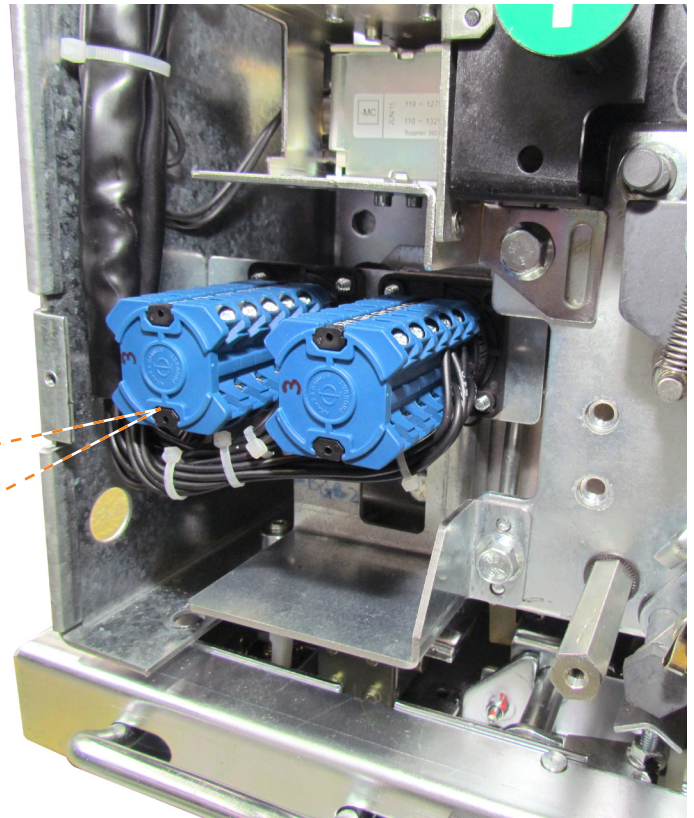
Vista do conjunto de montagem dos contatos auxiliares
